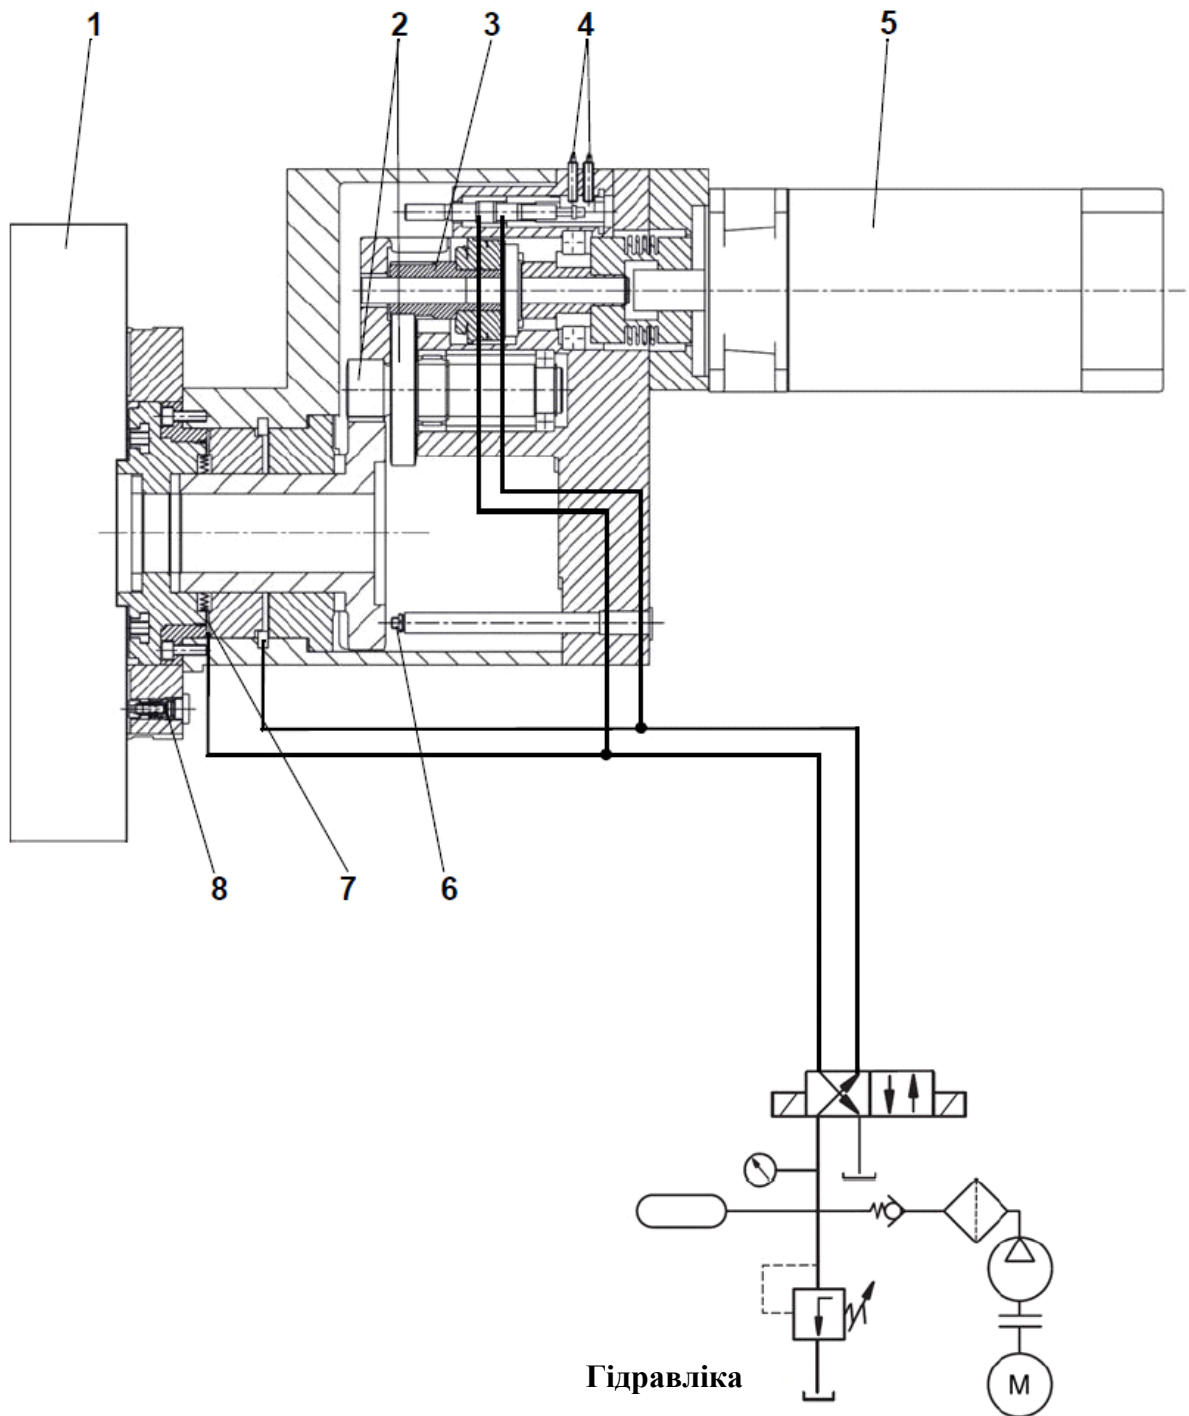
Конструкція приводу інструментальної дискової револьверної головки
